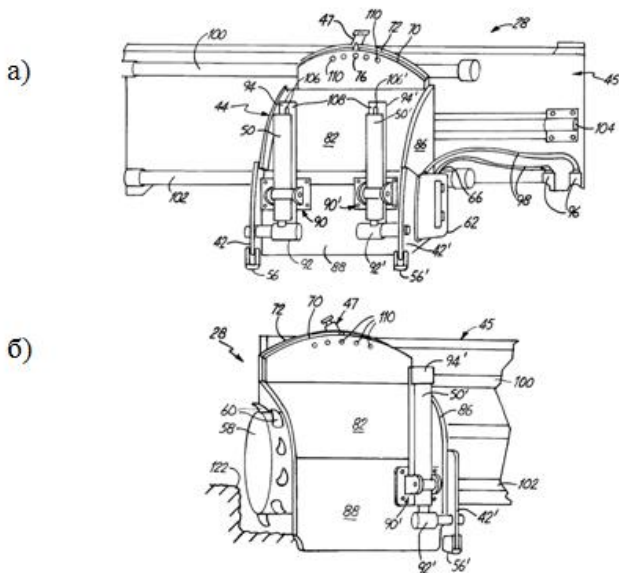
Схема механизма продольного перемещения и наклона фрезерного барабана [2]:
